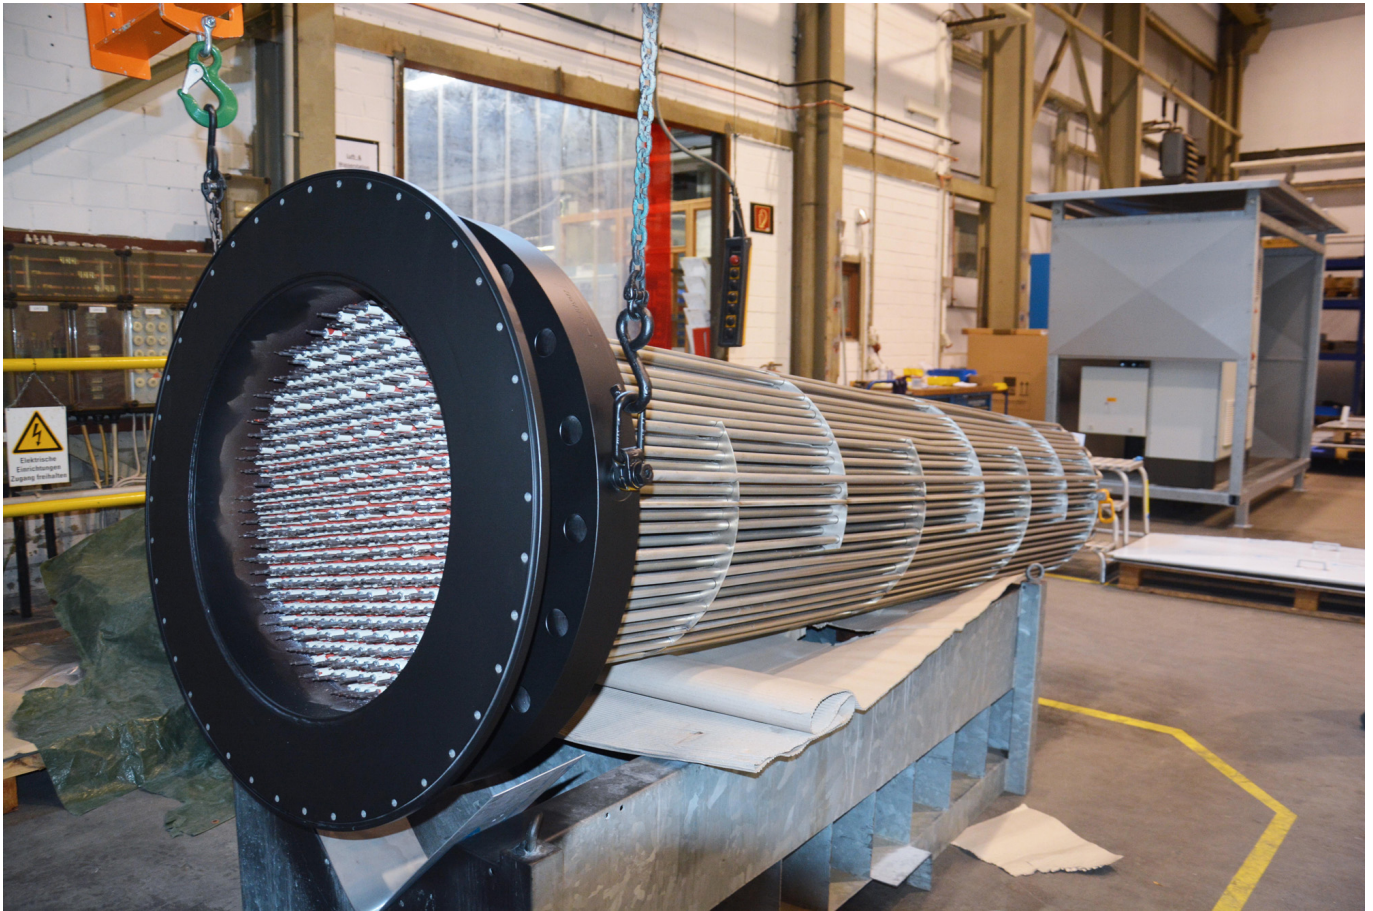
Explosionsgeschützte Wärmetechnik von Schniewindt. Zum Erwärmen von Schweröl für Schiffsdieselmotoren.
